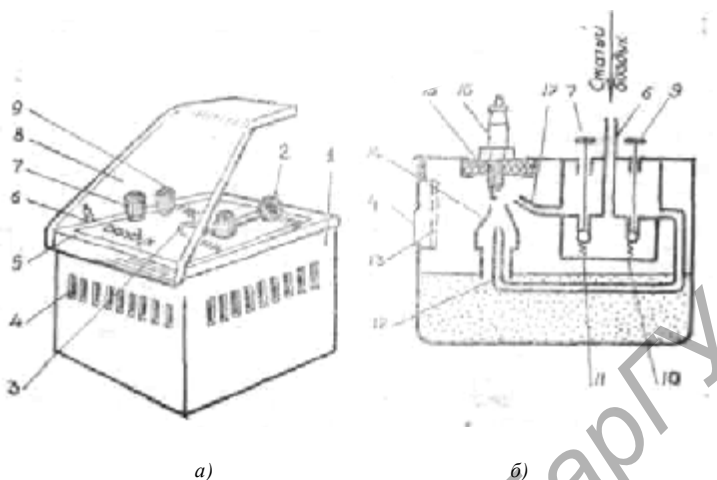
Приспособление Э-203-0 для очистки свечей зажигания от нагара: *a* — общий вид; *б* — пневматическая схема:
